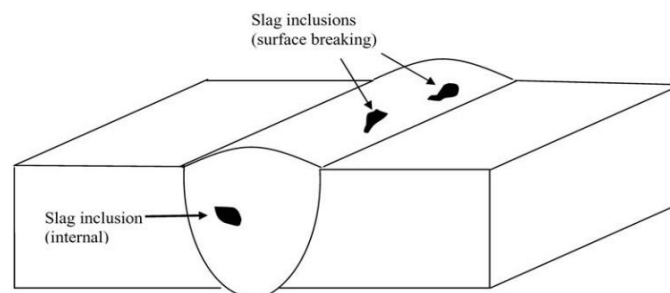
Porosidade em cordões de Soldadura (Inclusões Sólidas) [9]
